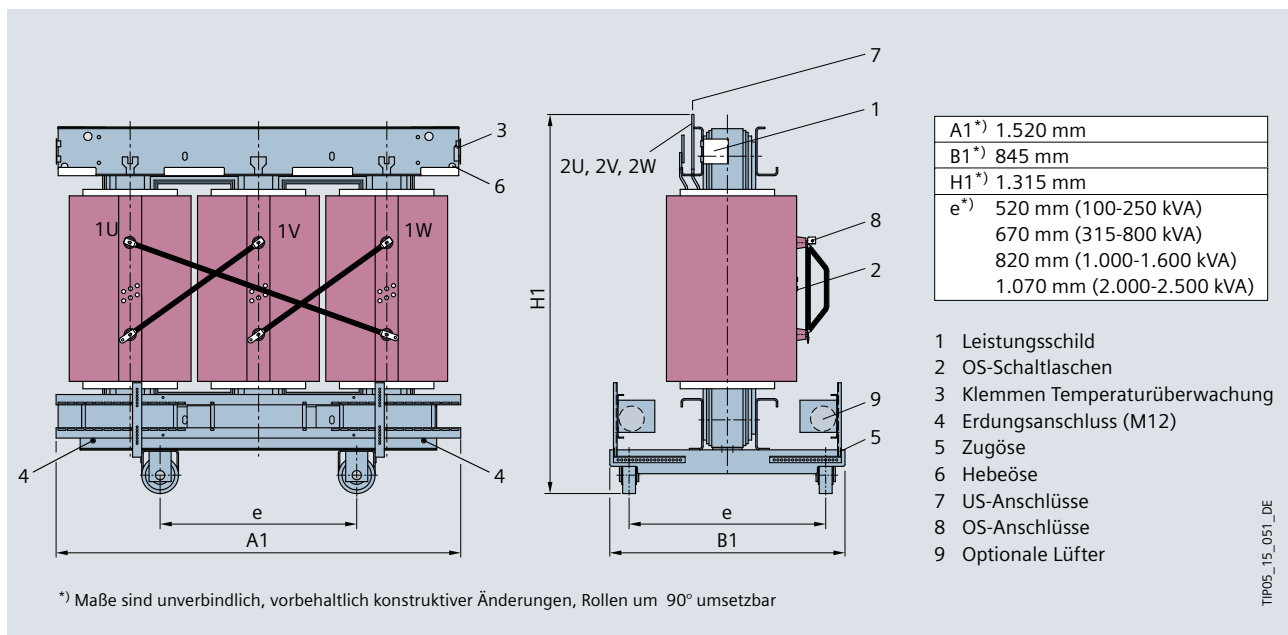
/2: CAD-Ansichten für GEAFOL-Transformator aus SIMARIS project
